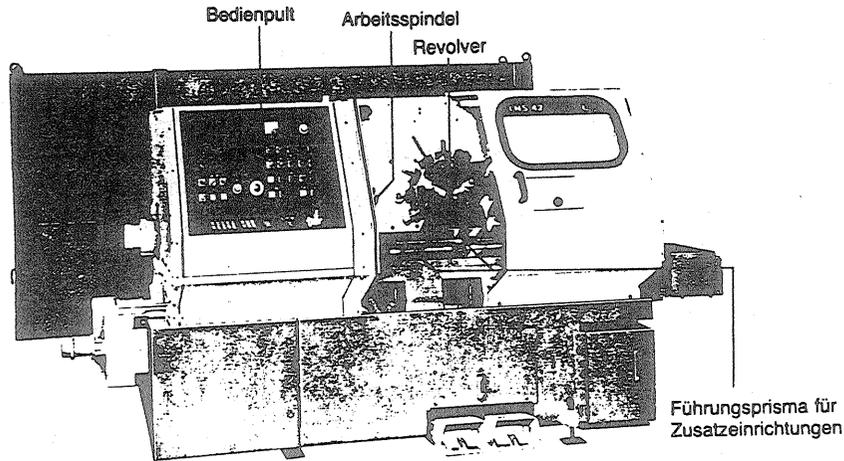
zeigt beispielhaft eine CNC-Drehmaschine mit einer modernen Handeingabesteuerung, die weitgehend gemäß DIN 66025 programmiert wird. Die Steuerung besitzt als Zusatzbausteine eine Vermessung der Werkzeugkorrekturwerte Q und L in der Maschine sowie eine graphisch-dynamische Simulation des Arbeitsablaufes am Bildschirm der Steuerung.
